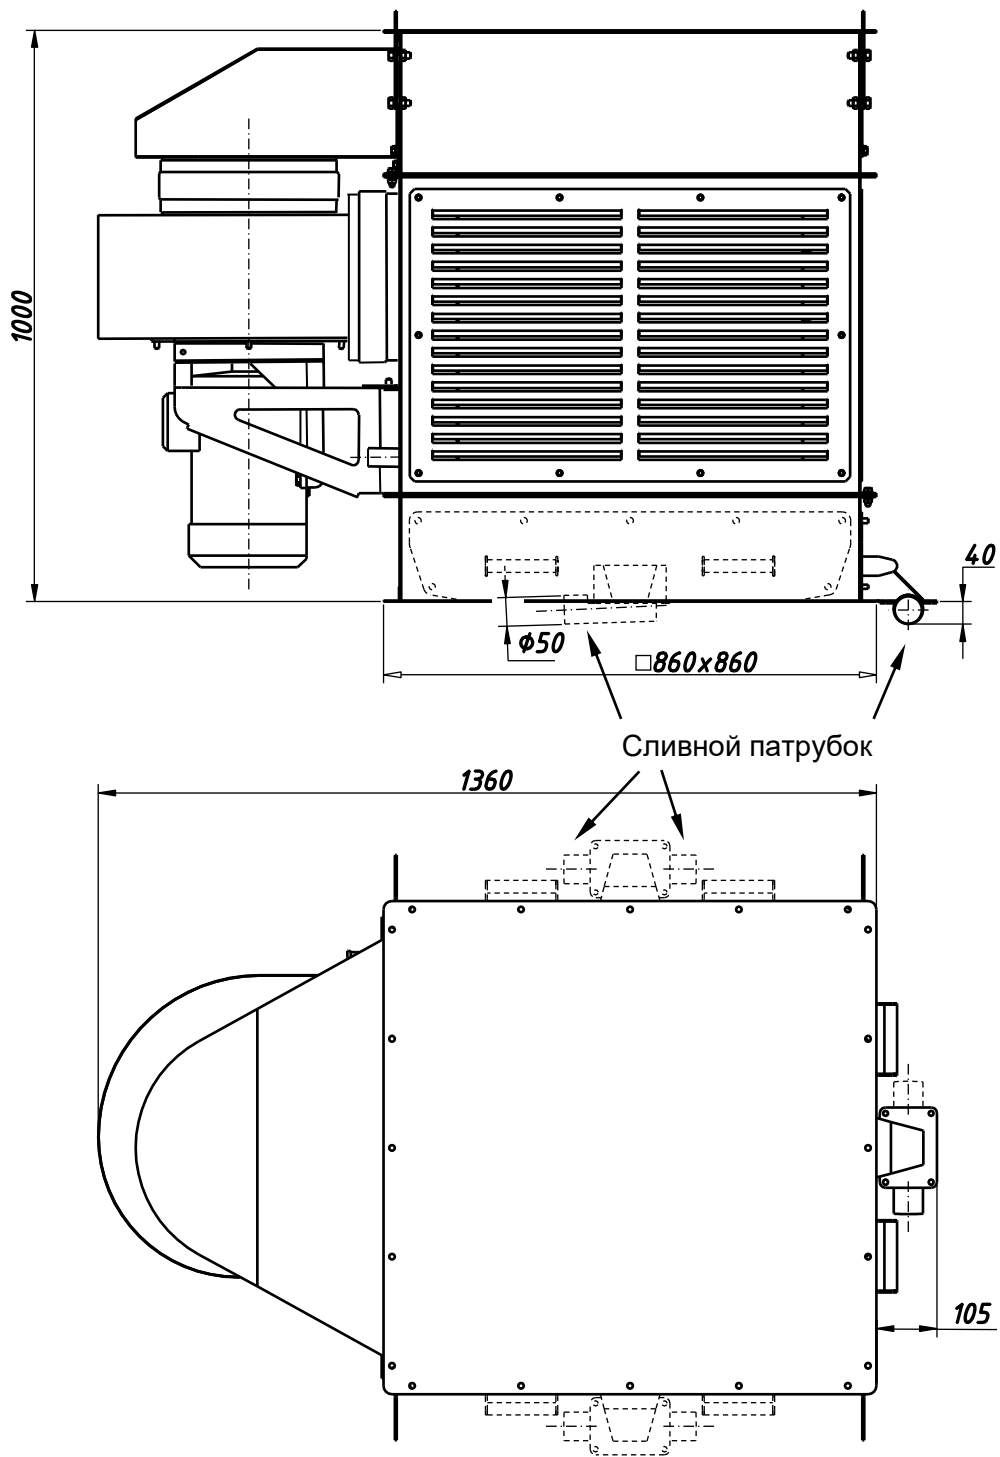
Общий вид и габаритные размеры МВГ (без дозатора).
